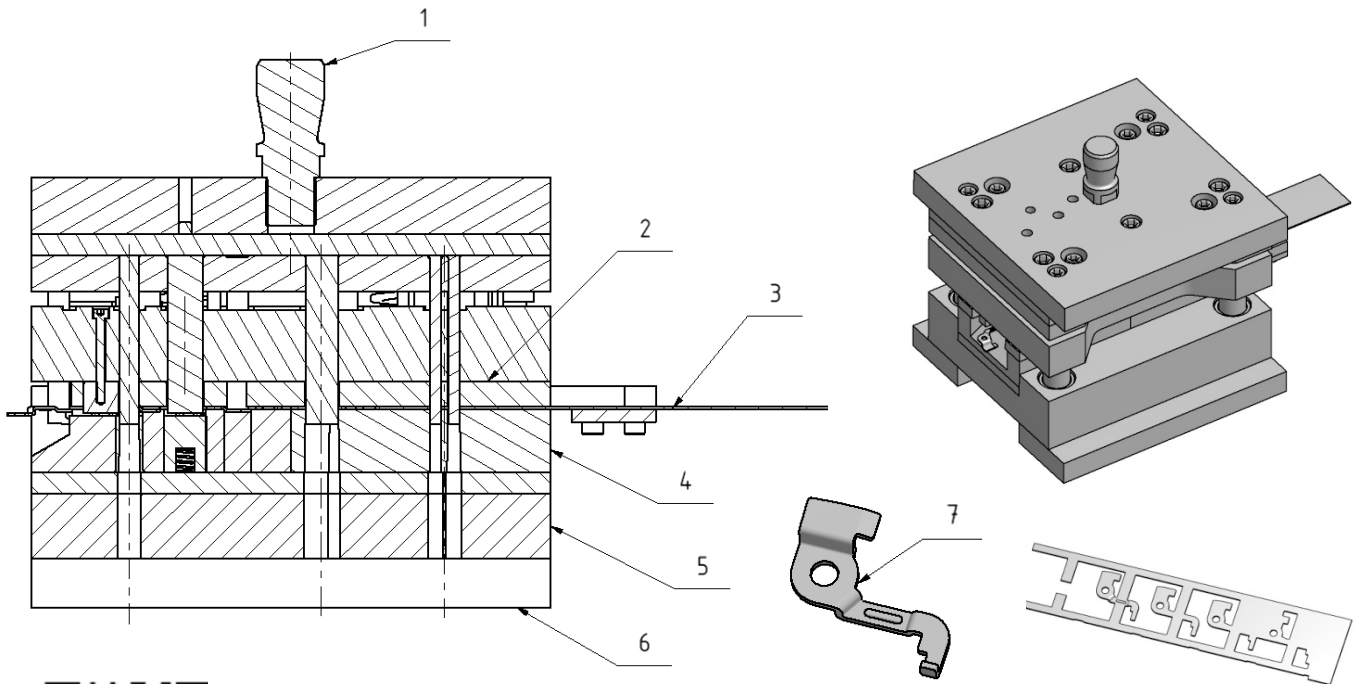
Ausstanz-Biegewerkzeug für Schnellspanner
